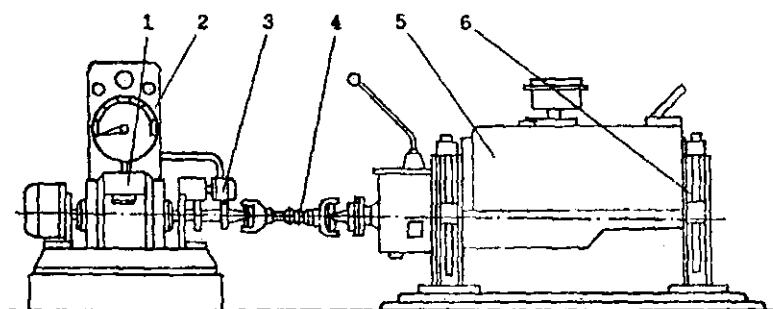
7. Стенд для приработки и испытания двигателей: 1-асинхронный электродвигатель, 2-щиток с приборами, 3-привод тахометра, 4-соединительный вал, 5-испытываемый двигатель, 6-опоры для установки двигателя.
